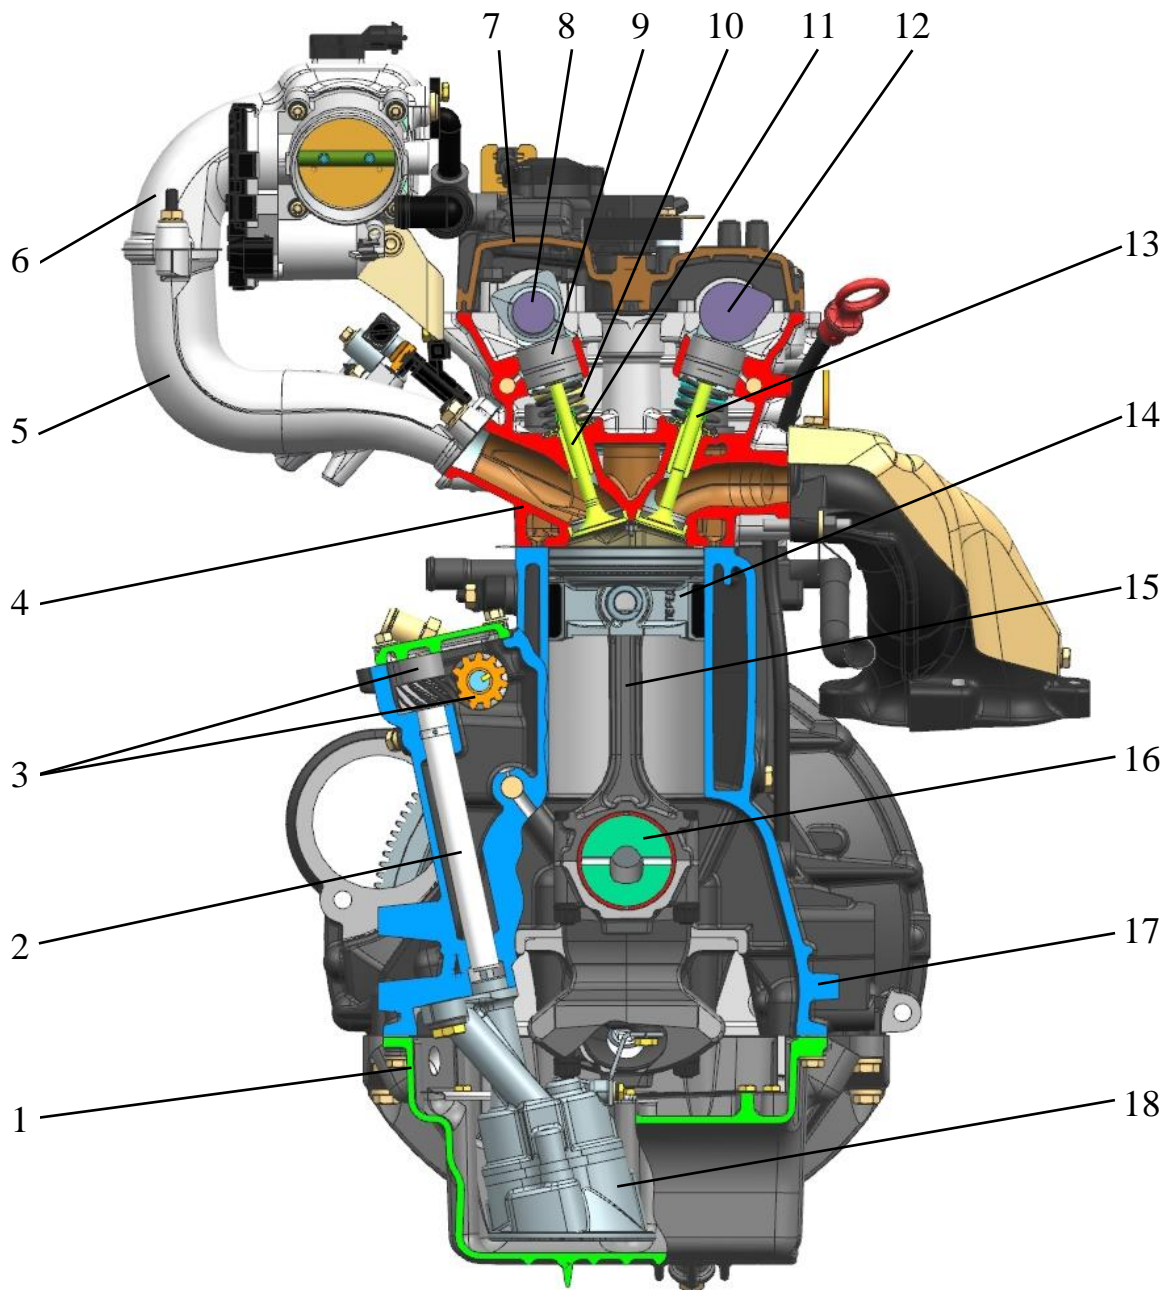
Поперечный разрез двигателя ЗМЗ-40905.10:
